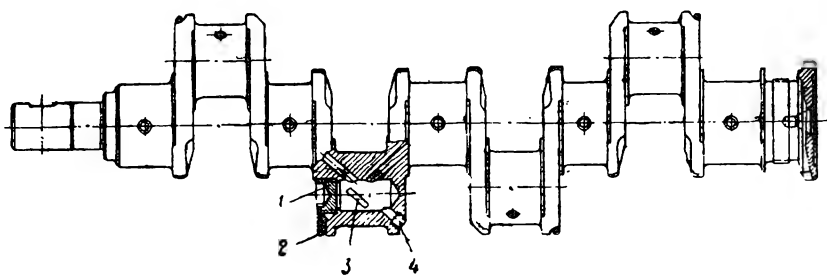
Коленчатый вал с центробежной очисткой масла:
